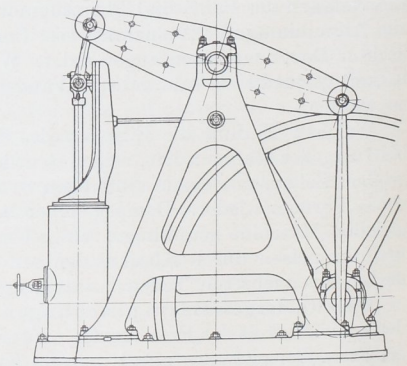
A-Rahmen einer Schwinghebelmaschine.
